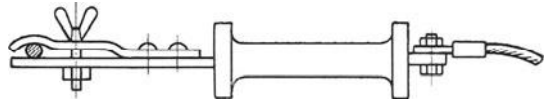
Schweißkolben für Warmschweißungen.
